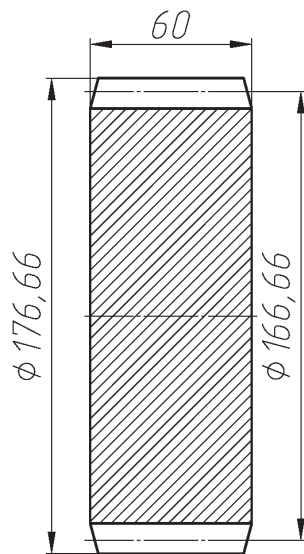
Изображение заготовки главного вида зубчатого колеса
